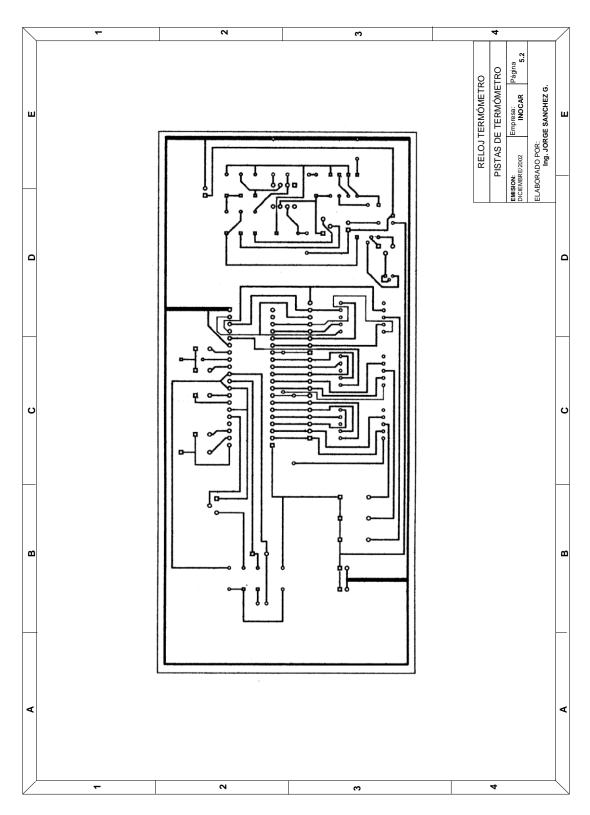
Tarjeta del termómetro (diagrama de pistas lado de soldadura)
